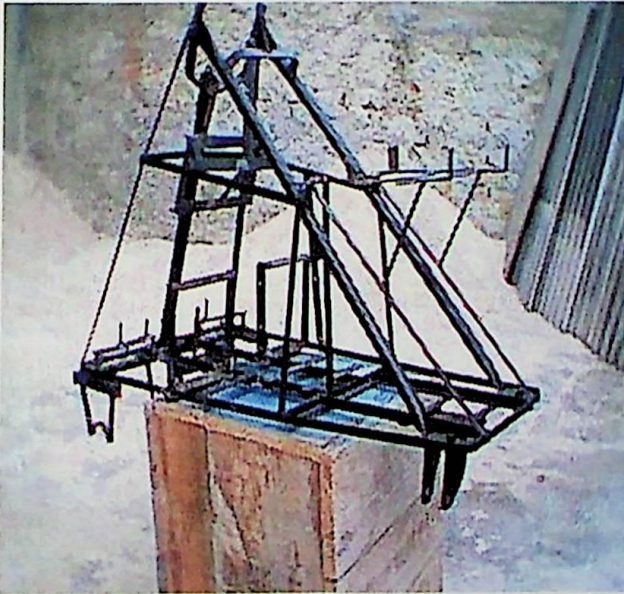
Chassis pronto para receber a pintura de fundo.
